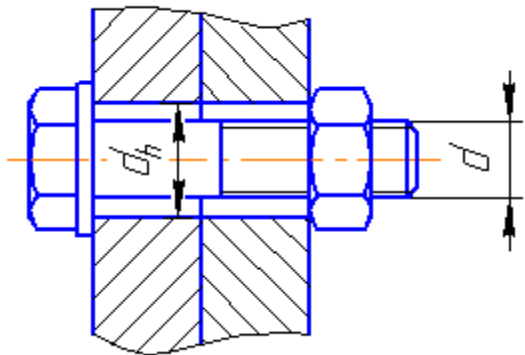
Конструктивный зазор между стержнем болта и отверстием в деталях
